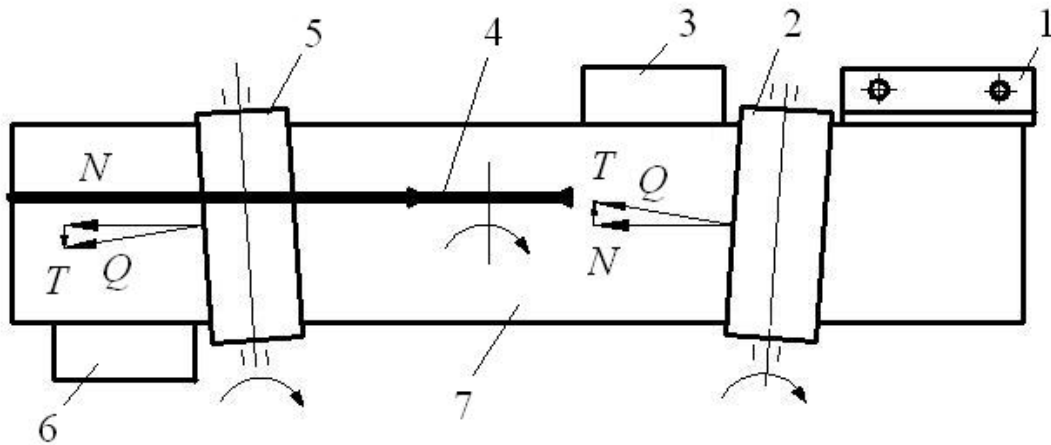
Схема продольного пиления заготовки на круглопильном станке с вальцовым механизмом подачи:
